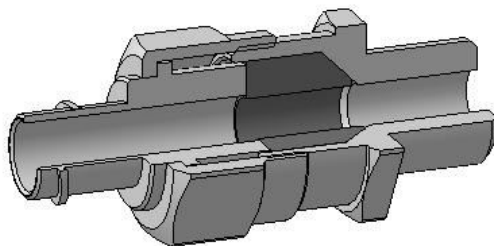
Конструкция кабельного ввода ВН с фитингом для монтажа кабеля в трубе
